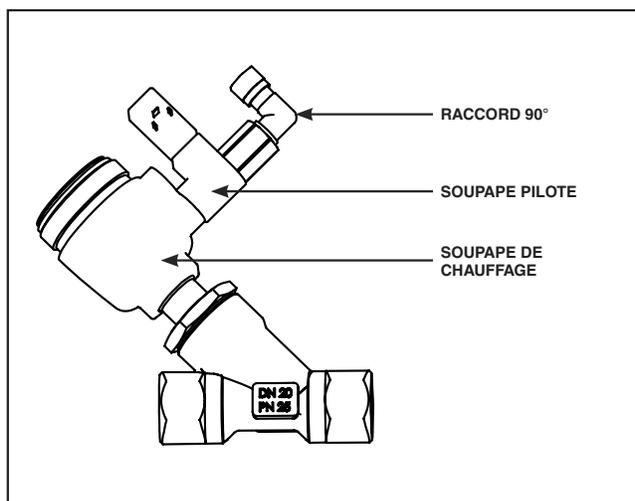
Assemblage d'une nouvelle soupape de chauffage
